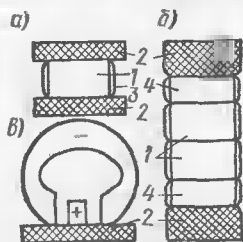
Схема монтажа гладких калибров — пробки (а, б) и скобы (в): 1 — калибр; 2 — изолирующий экран; 3 — хромовое покрытие; 4 — стальной защитный катод
